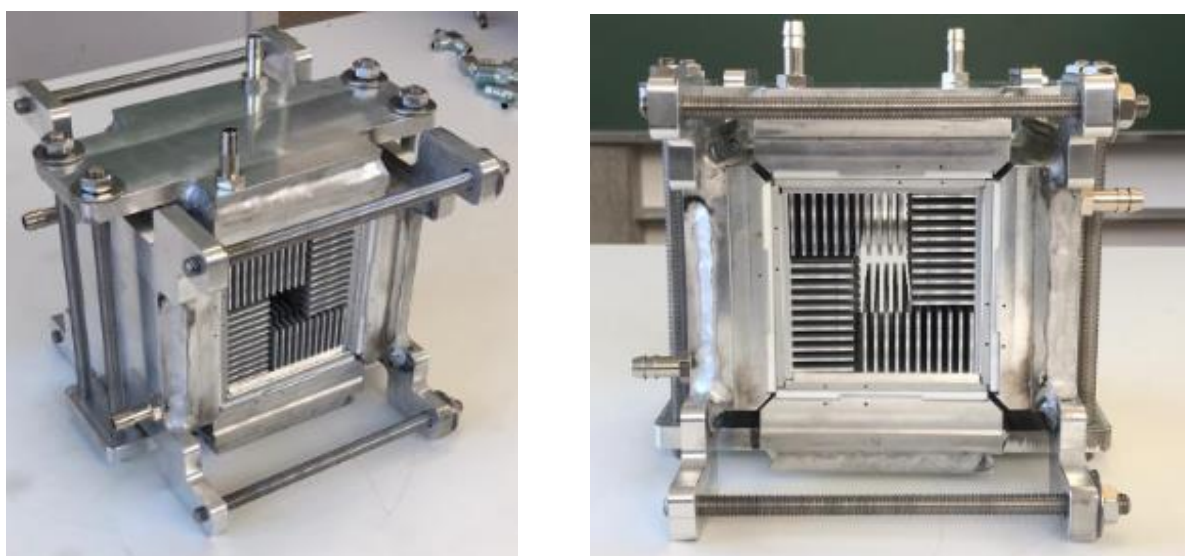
Assemblatge amb ràcords per les mànegues del Chiller.
